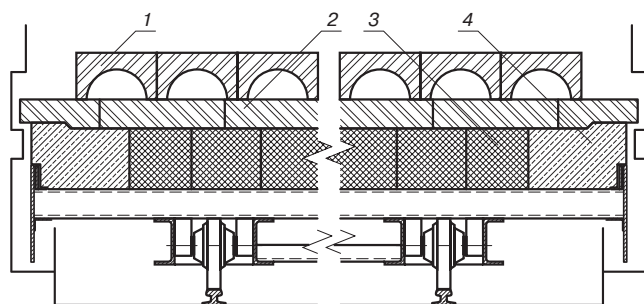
Структурная схема футеровки вагонетки: 1 — подовый канальный камень; 2 — керамобетонные плиты перекрытия; 3 — легкий изоляционный слой; 4 — жаростойкие легковесные блоки
